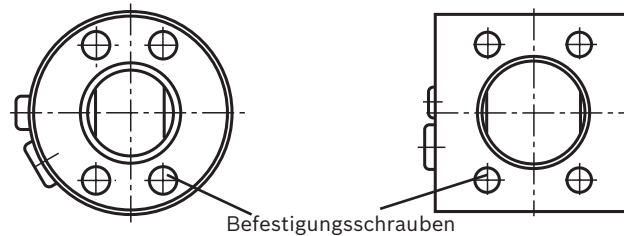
Befestigungsbohrungen: links (rund) für NG18, 28, 25; rechts (rechteckig) für NG 71, 100, 140, 180
